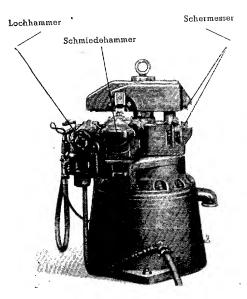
Rückansicht der Maschine Задияя сторона манины Rear view of machine Vue arrière de la machine Máquina vista desde atrás
